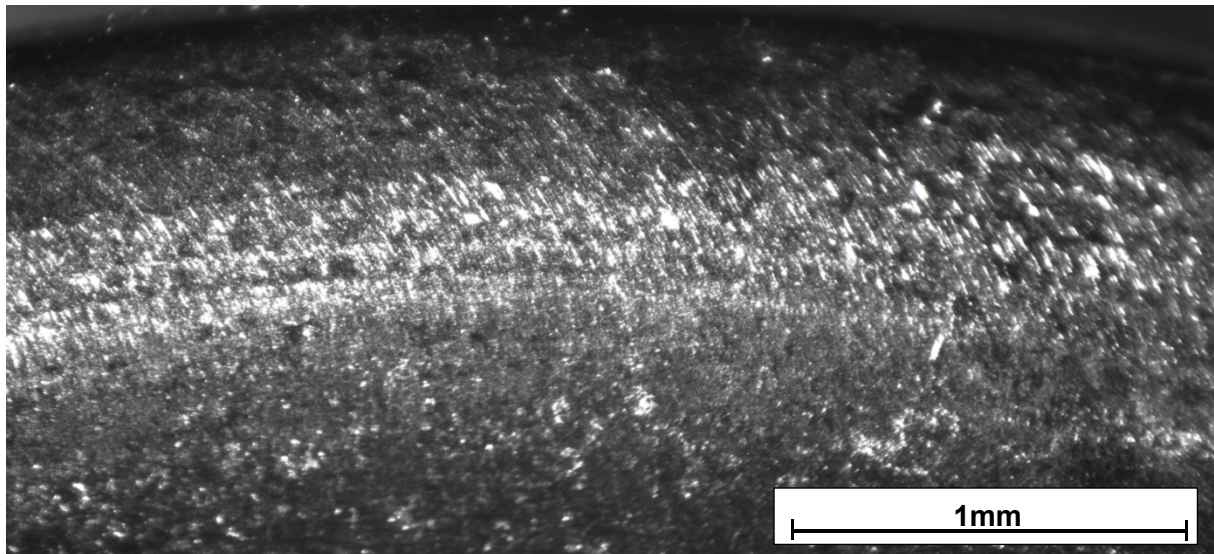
Gleitfläche der Trapezgewindespindel des Zustands „+C“
